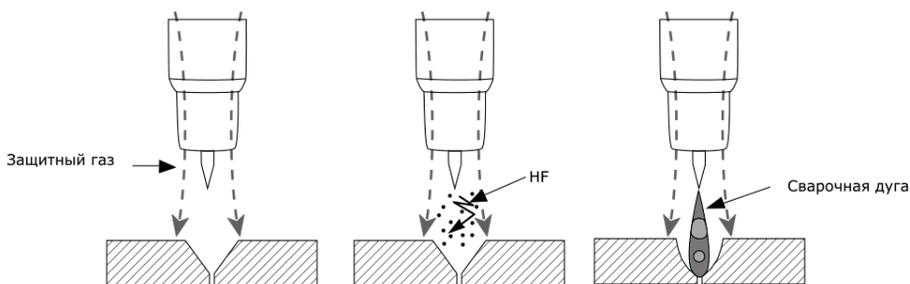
Процесс образования сварочной дуги.
